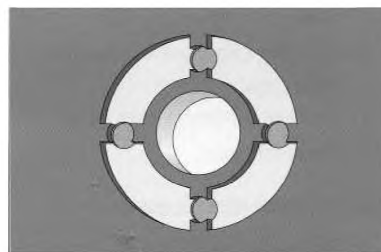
в – Фрезерование рядом с металлизированным отверстием для разрушения перемычки
